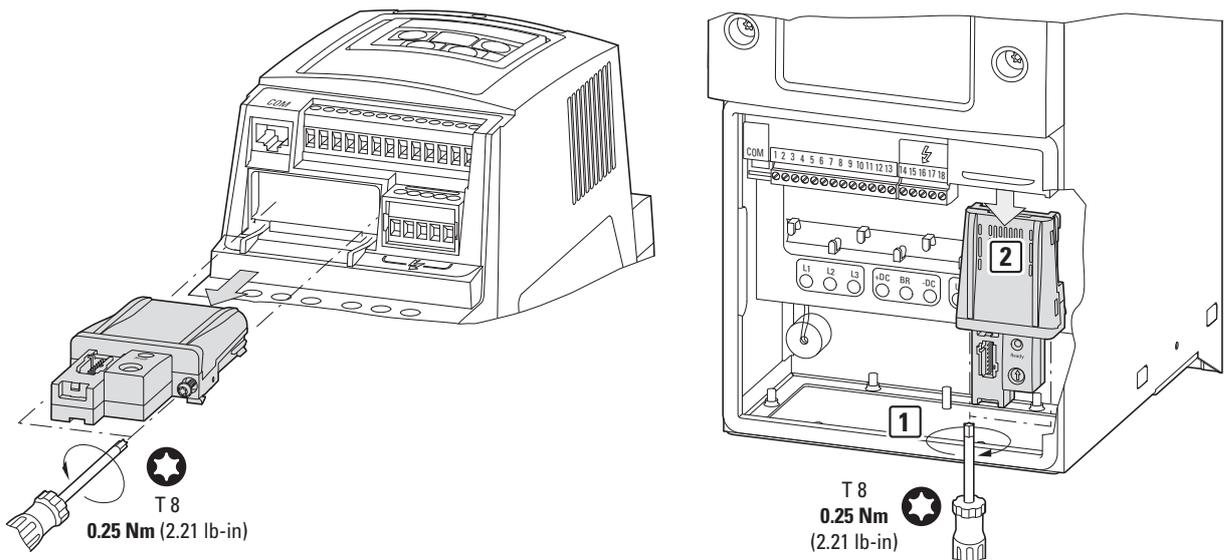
Anschaltung DX-NET-SWD1 entfernen (links: IP20, rechts: IP55)
